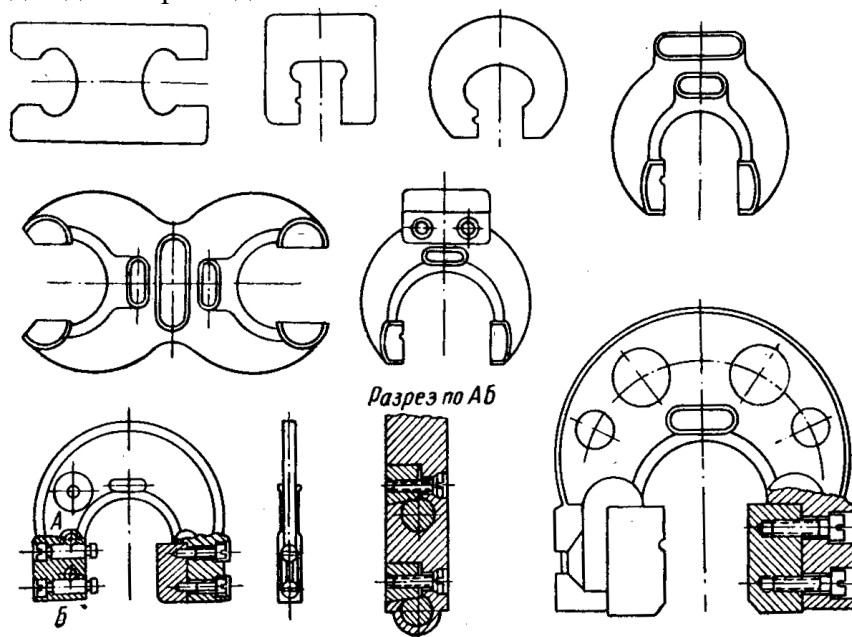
Гладкие калибры-скобы и их конструкции
